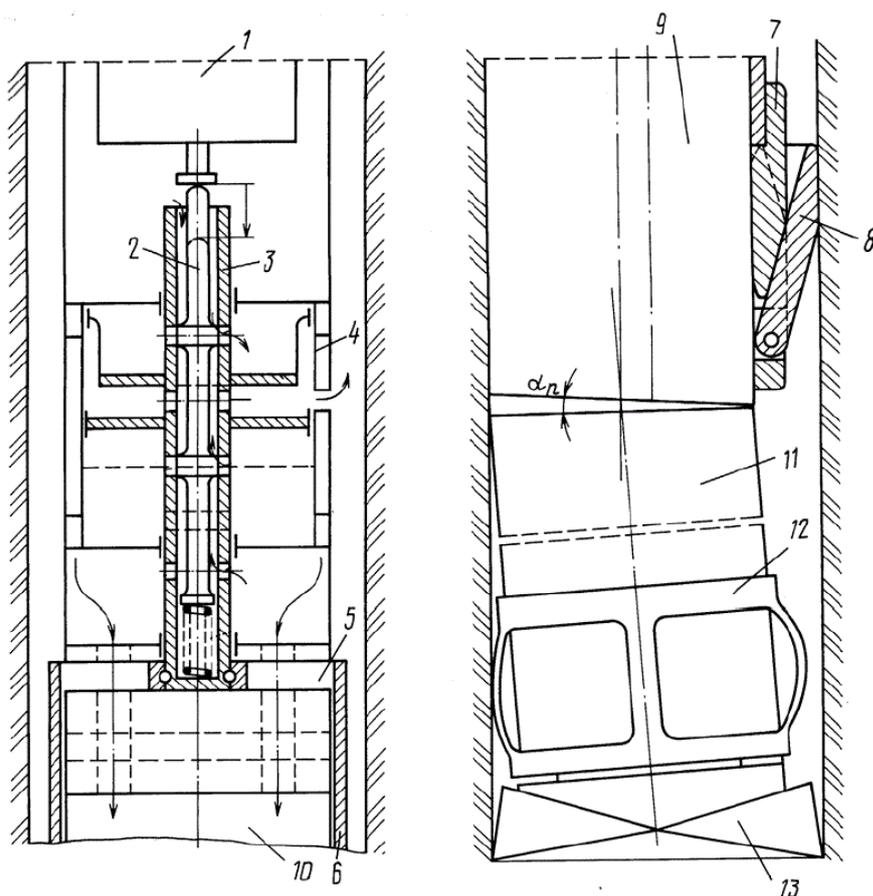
Устройство для перегиба частей забойного двигателя
